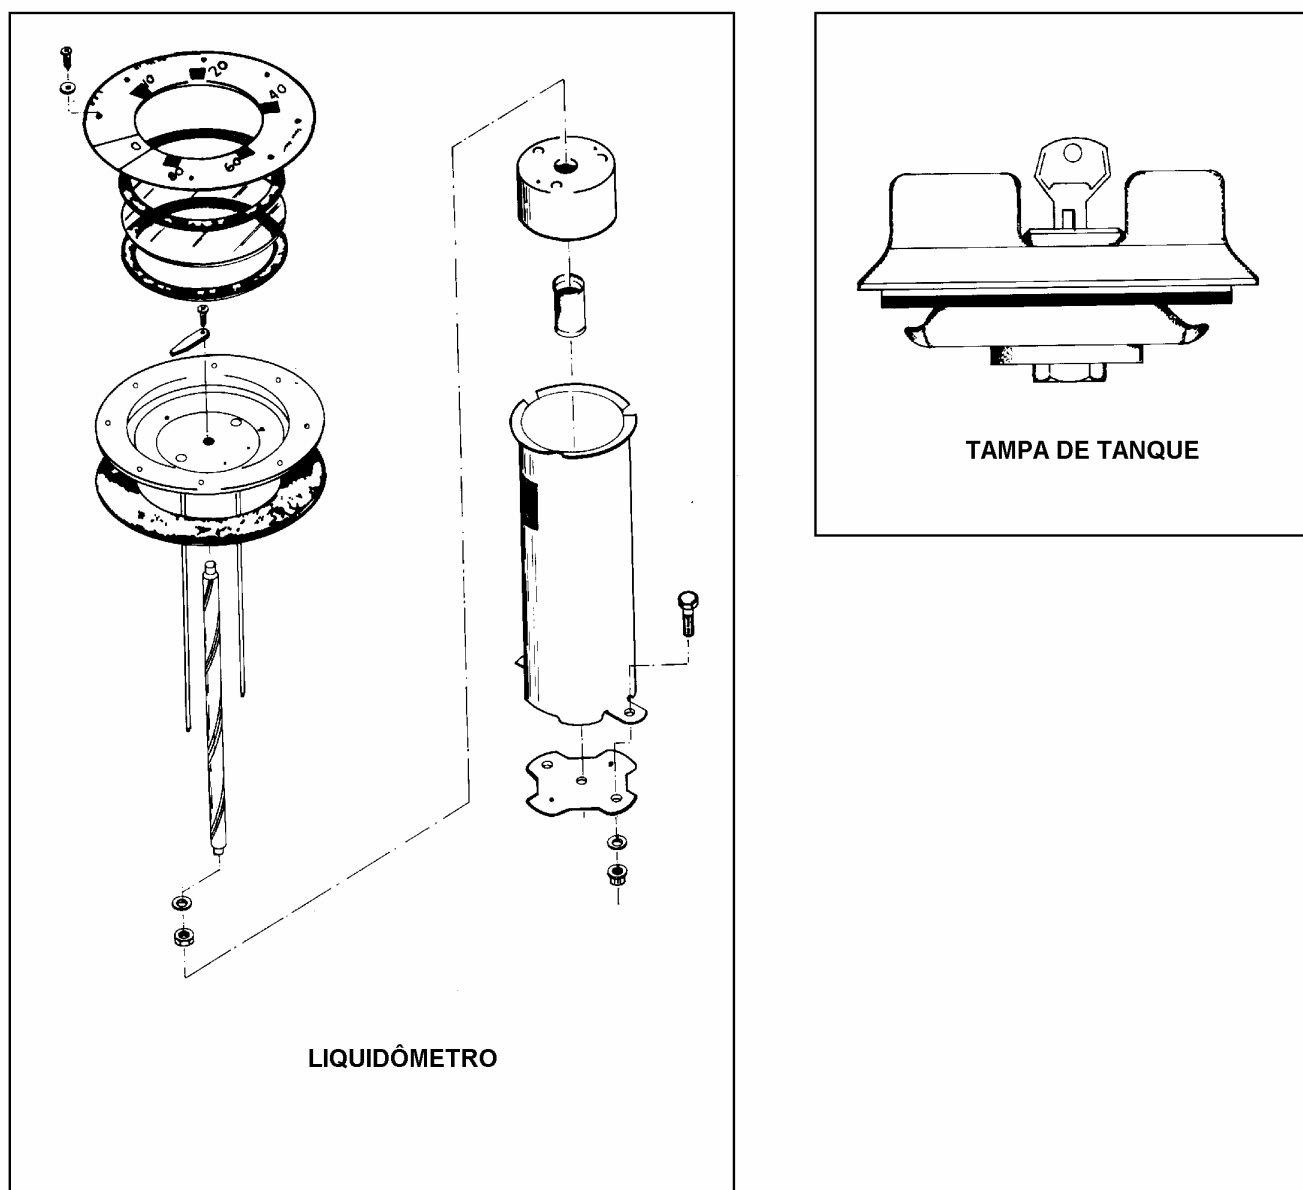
Instalação do Tanque de Combustível (Folha 2 de 2)
